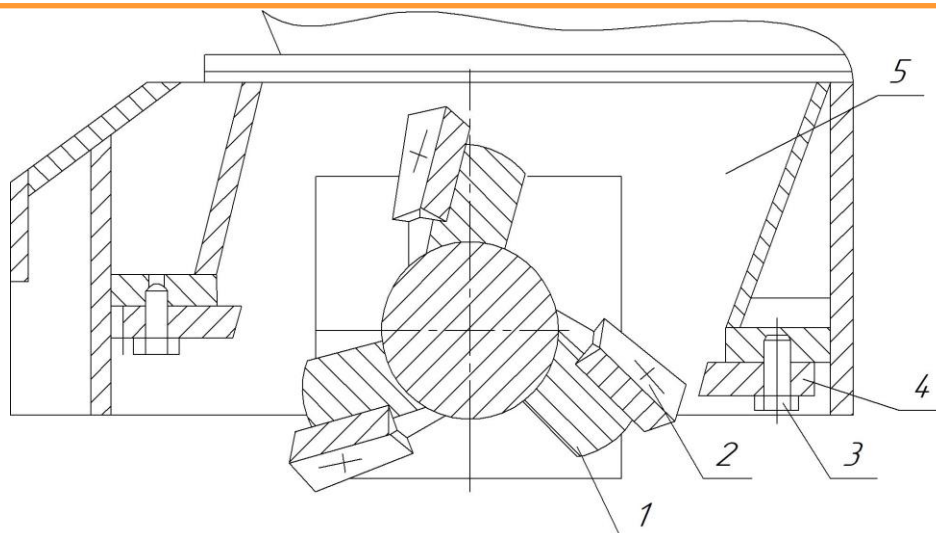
Роторно-ножевой барабан (разрез Б-Б)
